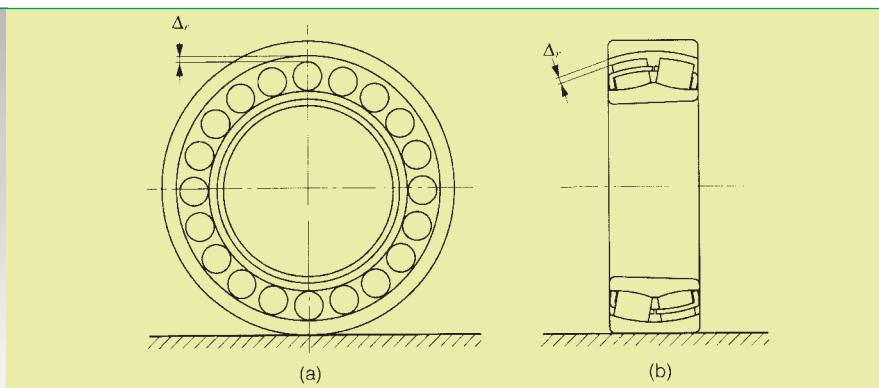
Medição de Folga no Rolamento Autocompensador de Roos
